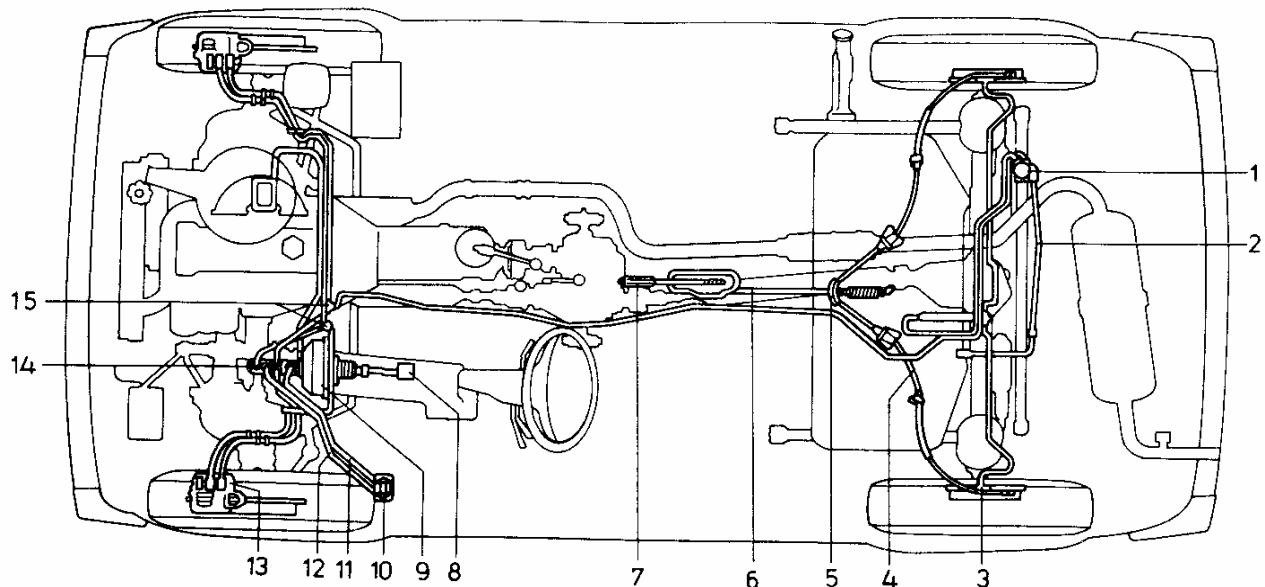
Esquema del sistema de frenos: 1 - regulador de la presión; 2- palanca de torsión del regulador de la presión; 3- cilindro de rueda del freno trasero; 4- cable trasero del freno de estacionamiento; 5- equilibrador del cable trasero; 6- cable delantero del freno de estacionamiento; 7- palanca del freno de estacionamiento; 8- pedal del freno; 9- servo a vacío; 10 - tanque del hidroaccionamiento de los frenos; 11 - circuito primario de freno; 12- circuito secundario de freno; 13- bloque de cilindros del freno delantero de disco; 14- cilindro principal de los frenos; 15- unión en T
